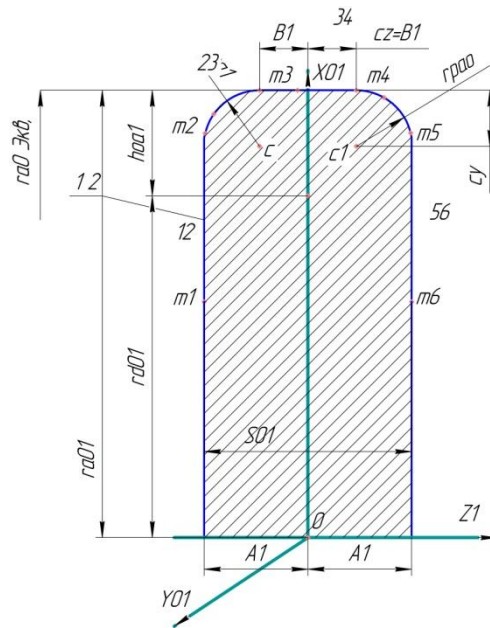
Твірний профіль вихідної інструментальної поверхні
